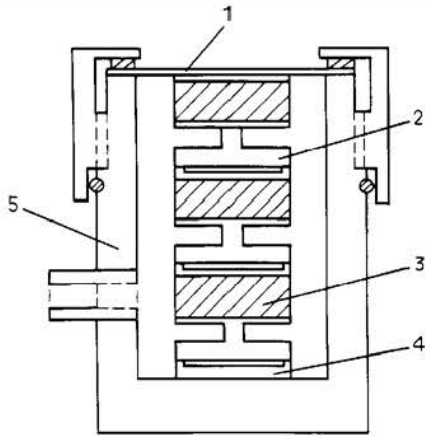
Конструкция трехзвенного излучателя: 1 — излучающая пластина, 2 — упругие балки, 3 — пьезопластины, 4 — опорные диски, 5 — корпус
